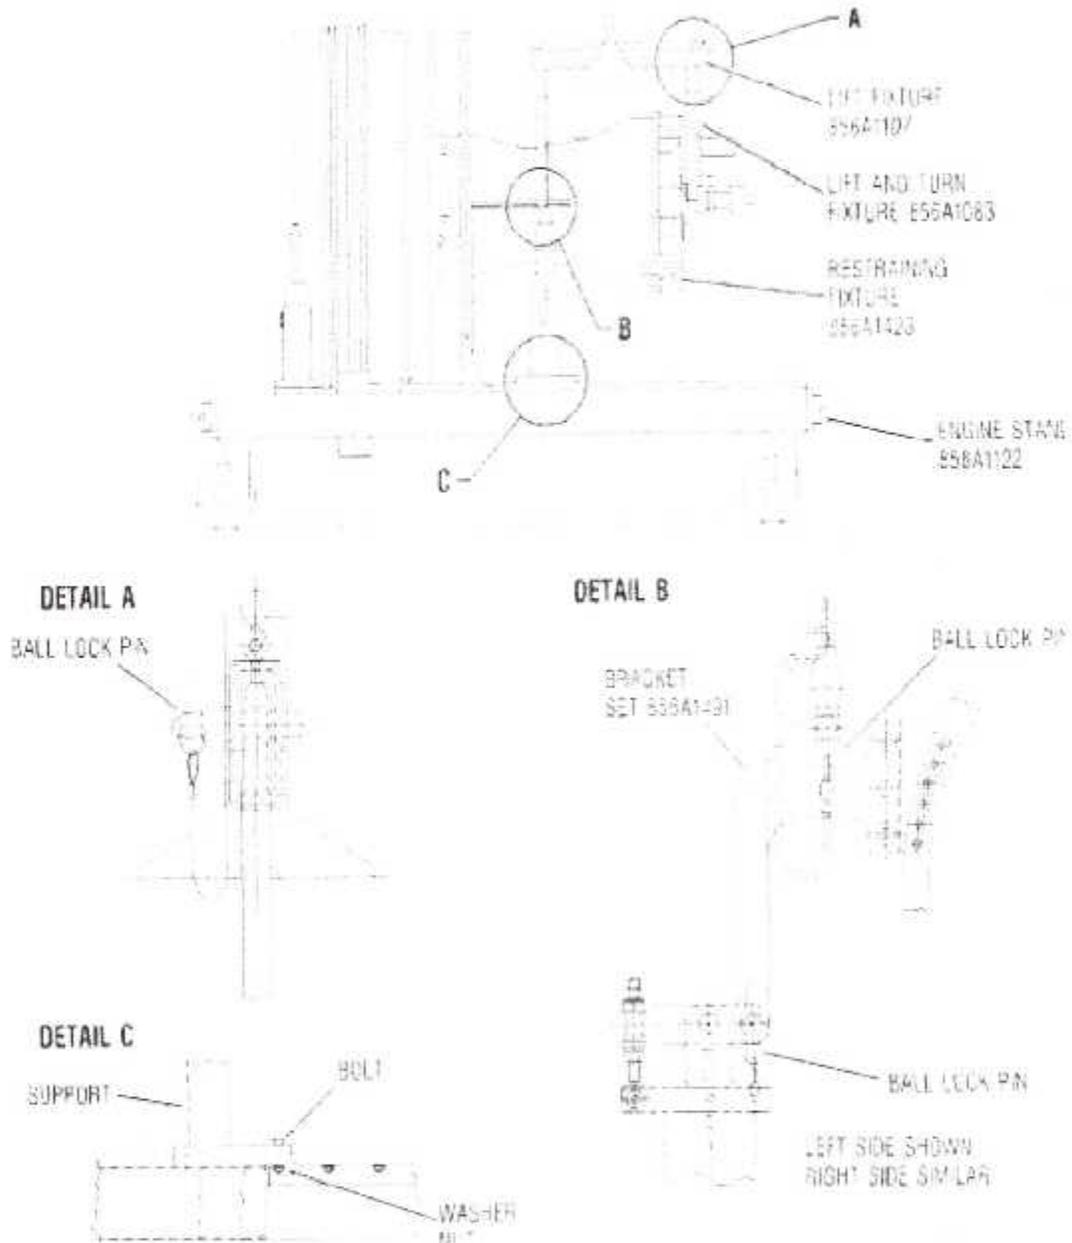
Installation la Poutre de Levage. 856A1107G07 sur le Major Core.
